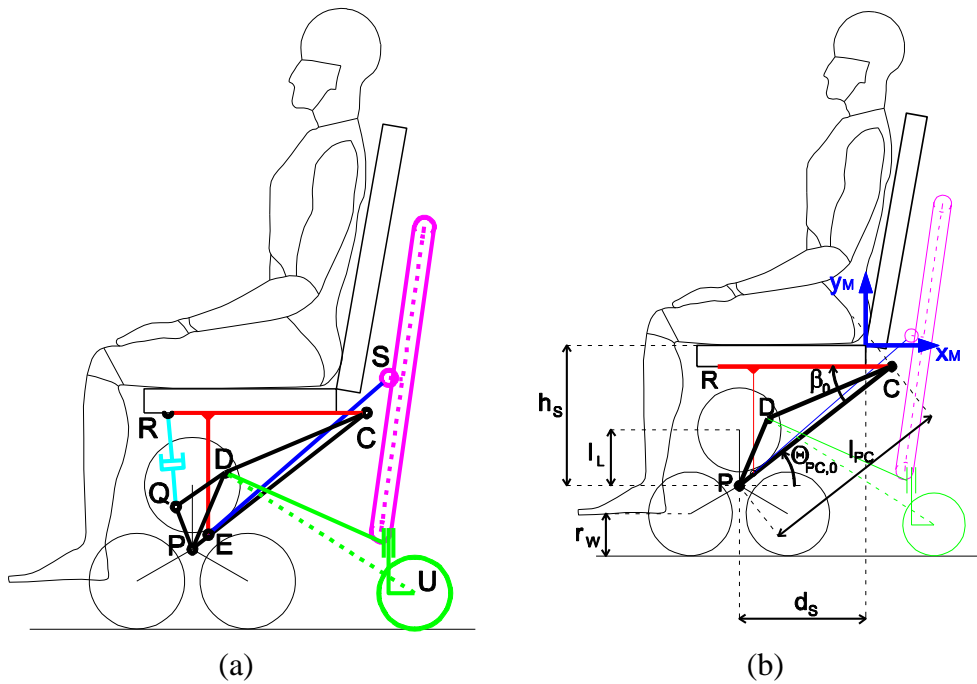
(a) Struttura cinematica complessiva della carrozzina; (b) Schema e dimensioni di riferimento per il sotto-telaio PC, il sotto-telaio RC e la sedia
